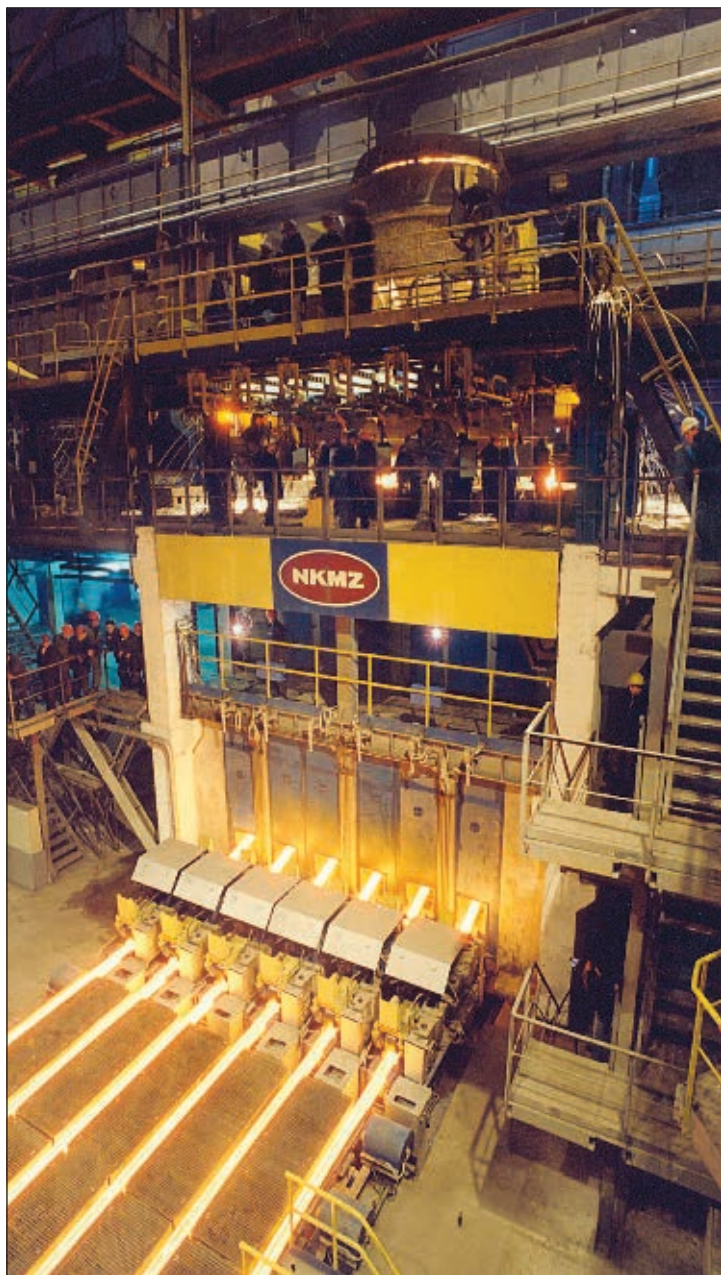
Шестиручьевая сортовая машина непрерывного литья заготовок
